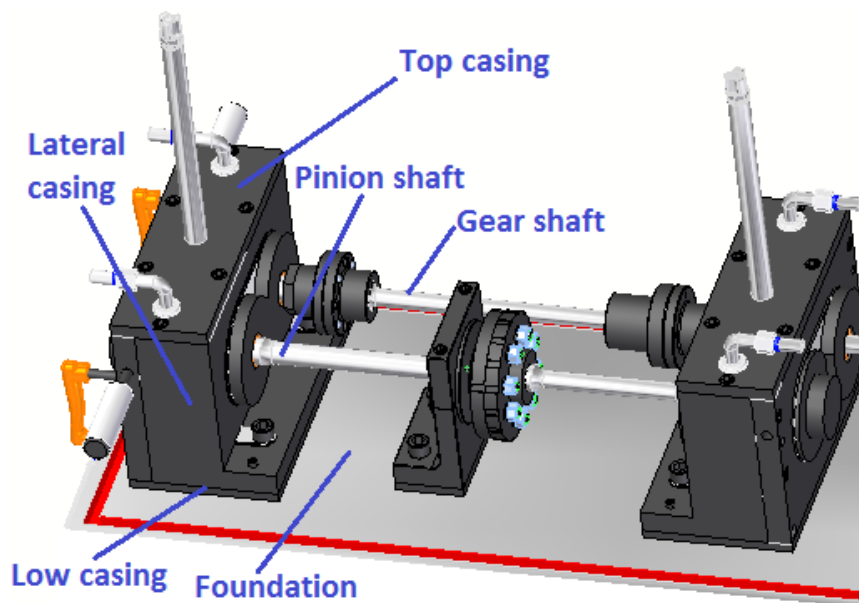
, Elementos externos de la caja de ensayos de engranajes: cada parte de la caja (*casing*), bancada (*foundation*), elemento cilíndrico de la parte superior de la caja y partes exteriores del eje del piñón y de la rueda (*pinion shaft*, *gear shaft*)
